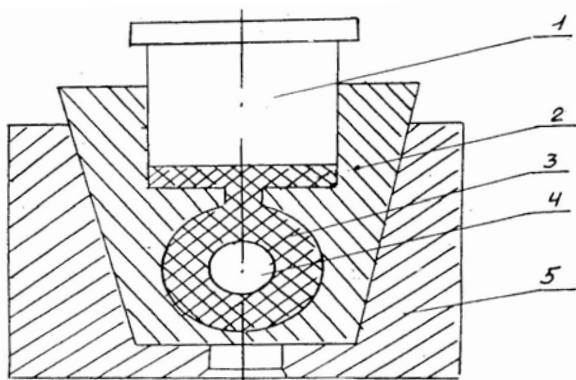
Пресс-форма литейного прессования с вертикальной плоскостью разъема, одногнездная: 1 – поршень; 2 – матрица; 3 – деталь; 4 – знак; 5 – обойма
